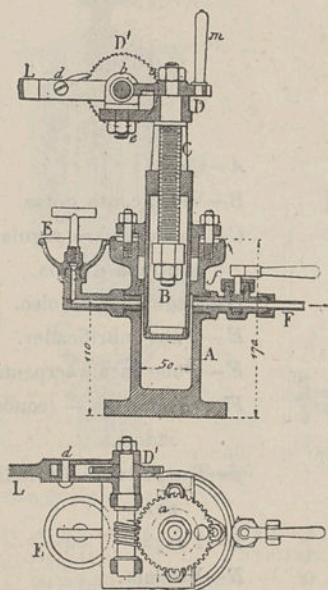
LUBRIFICADOR MECANICO MOVIDO PELA MACHINA
